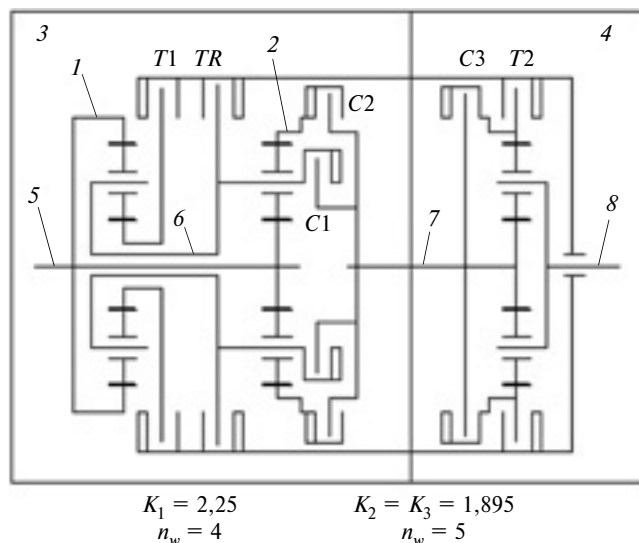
Новая кинематическая схема планетарной коробки передач:
